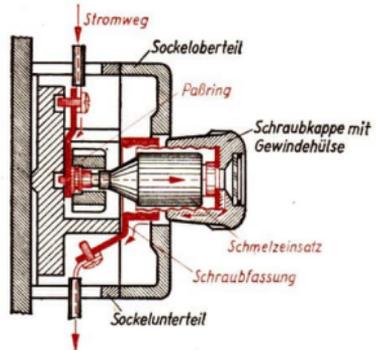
/2. Stromweg in einer Sicherungsanlage mit Schmelzsicherung: Kontaktplatte – Schmelzeinsatz – Gewinde des Deckels – Gewinde des Gehäuses
